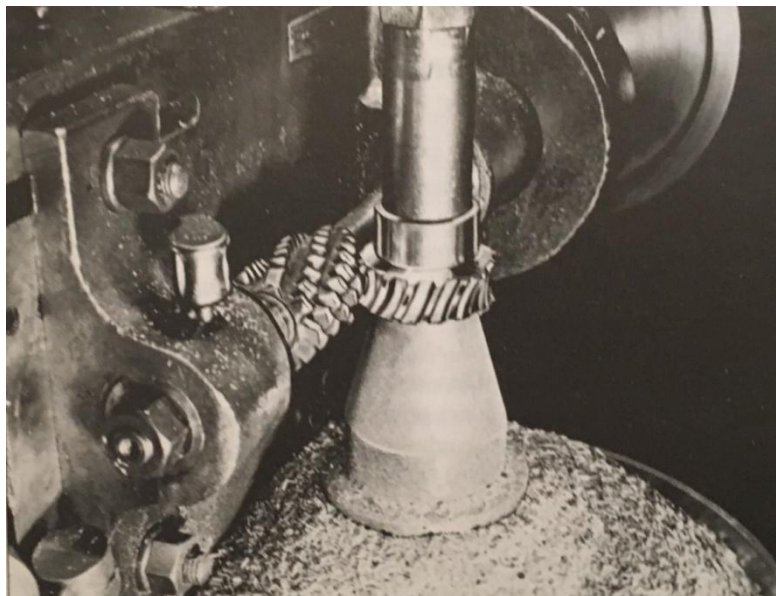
Fresagem de uma engrenagem cilíndrica helicoidal (Budynas, et al. 2011)
